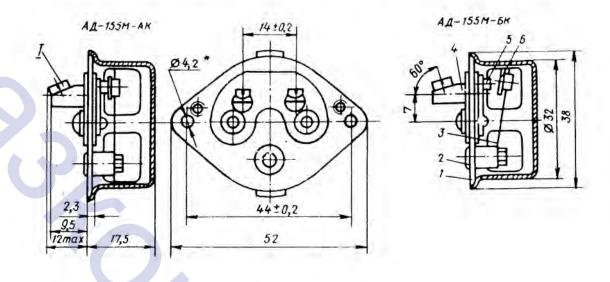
Термовыключатель типа АД-155М с защитным колпачком (размеры без допусков наибольшие):
